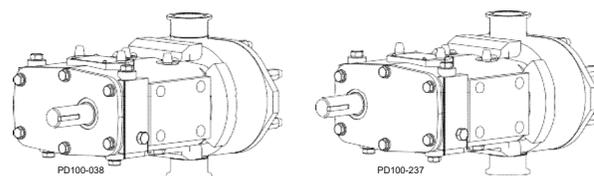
Montage latéral gauche et droit (vue depuis le couvercle de la pompe)
